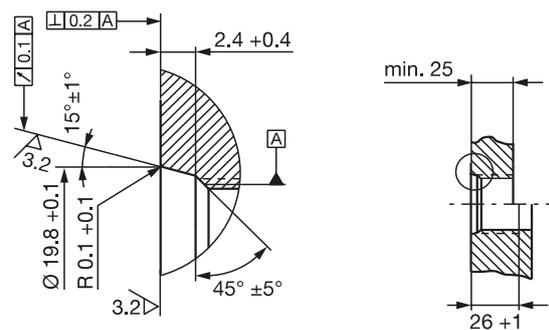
Einschraubloch M18x1.5 nach ISO 6149 O-Ring 15.4x2.1
